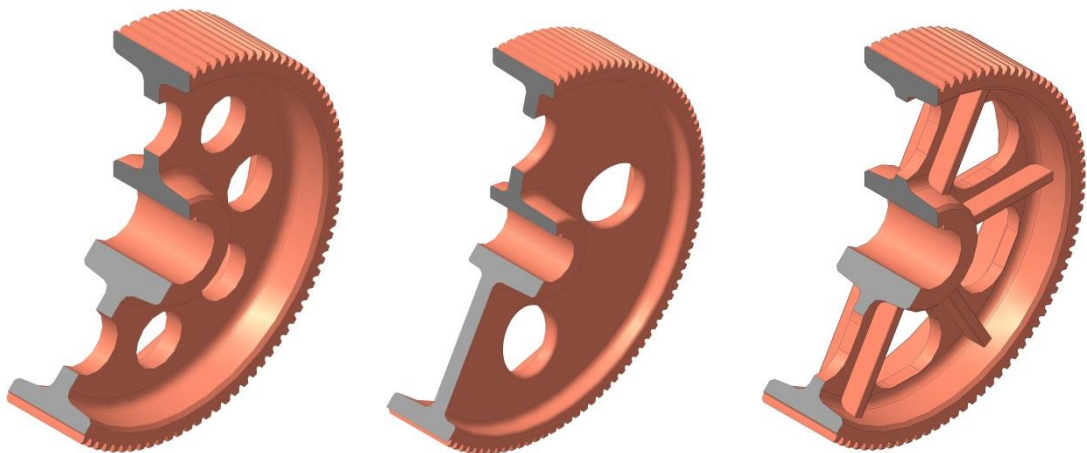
Зубчасті колеса виготовлені за допомогою литва
